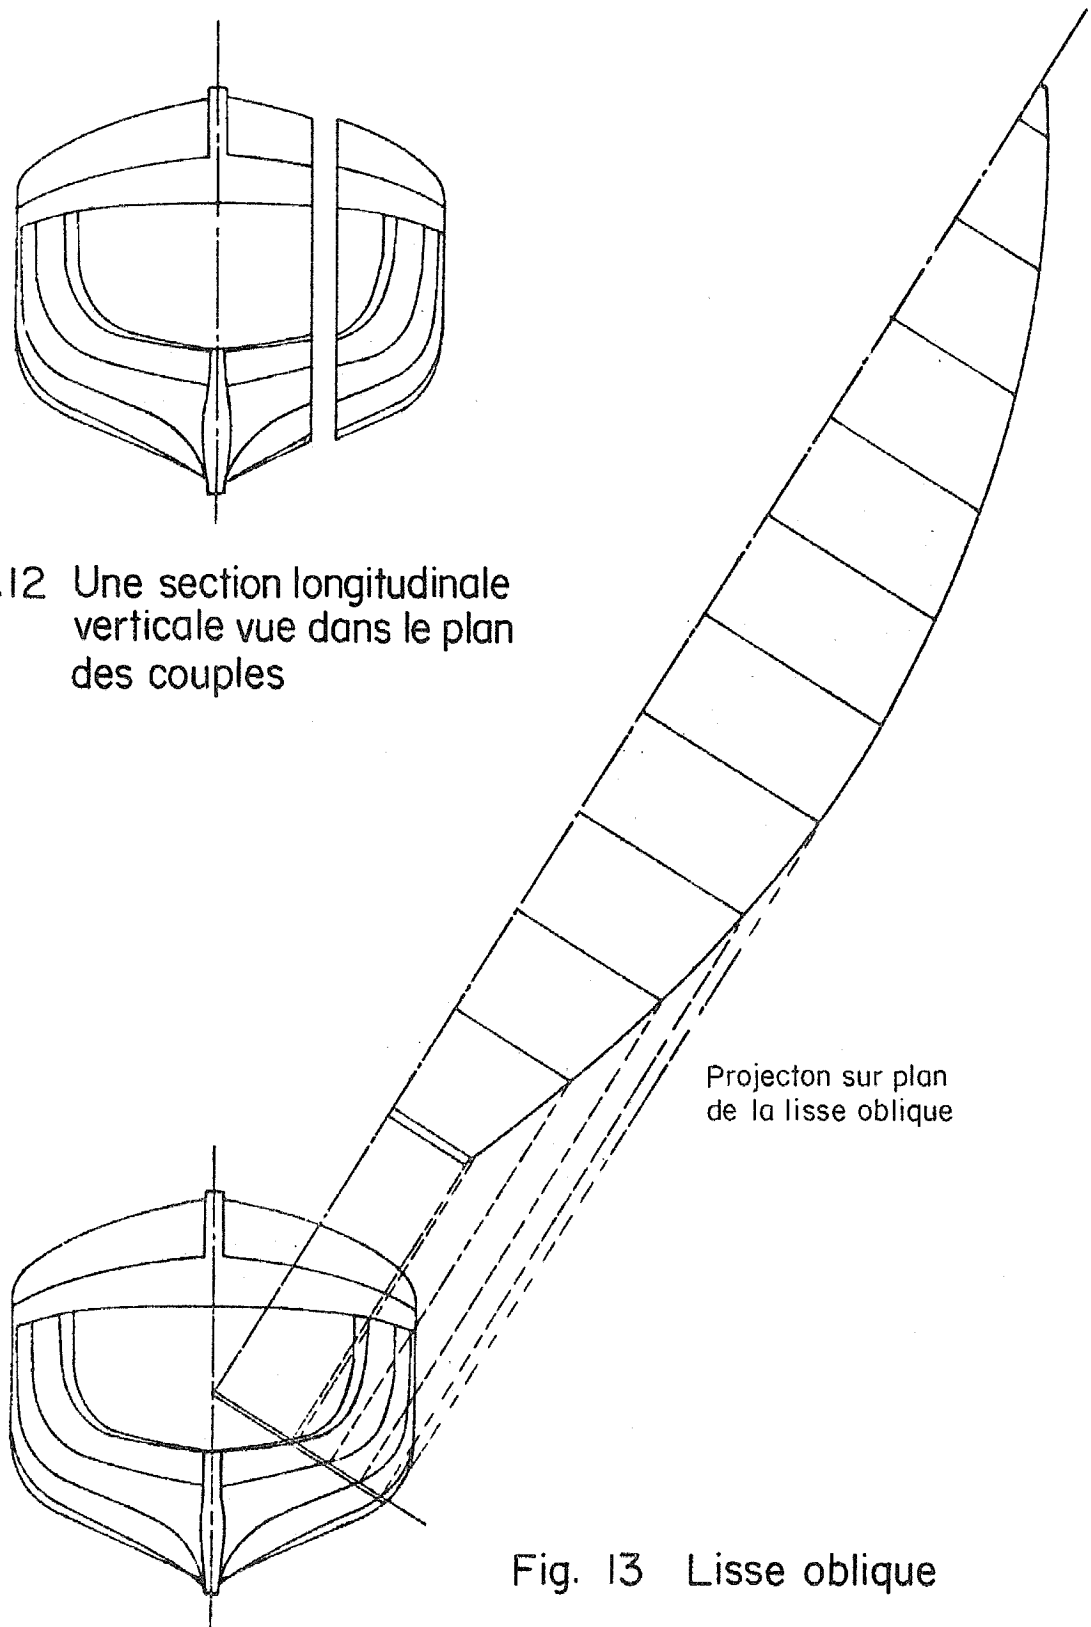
Une section longitudinale verticale vue dans le plan des couples
